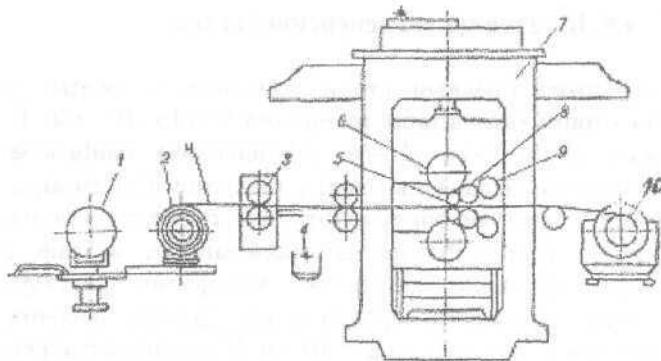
Схема реверсивного стана 250/1320×1400:
